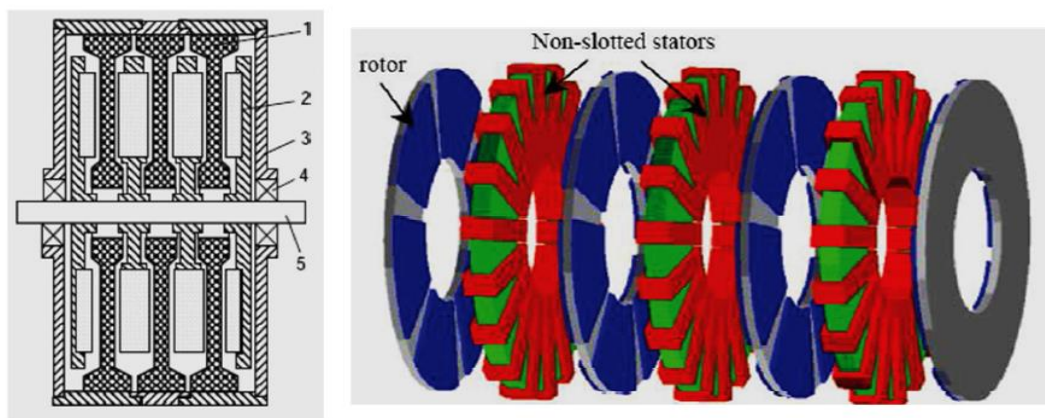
b : Descriptif de la machine à flux axial stator interne.
